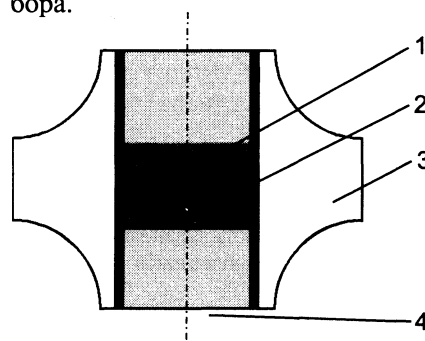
Вид контейнера высокого давления со спекаемой заготовкой: 1 – заготовка; 2 – трубчатый нагреватель; 3 – контейнер; 4 – теплоизолирующие заглушки
